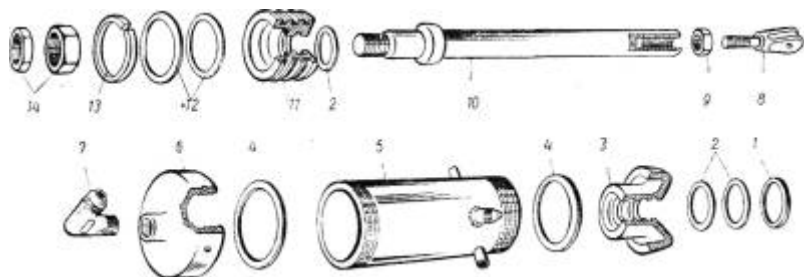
Типовой пневматический цилиндр управления клапаном и тормозом:
